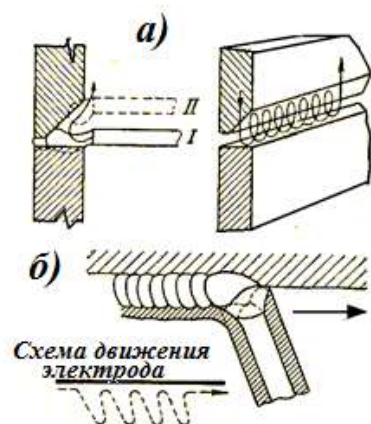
Сварка горизонтальных (а) и потолочных (б) швов
